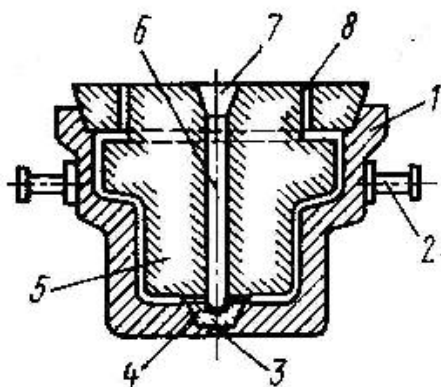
Конструкция вытряхного кокиля для алюминиевой отливки:
